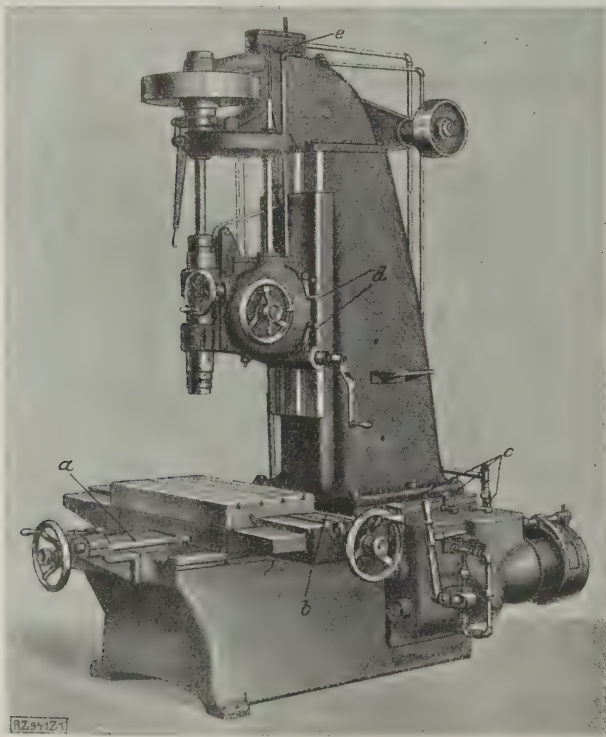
Vorrichtungs-Bohrmaschine von Pratt & Whitney.
